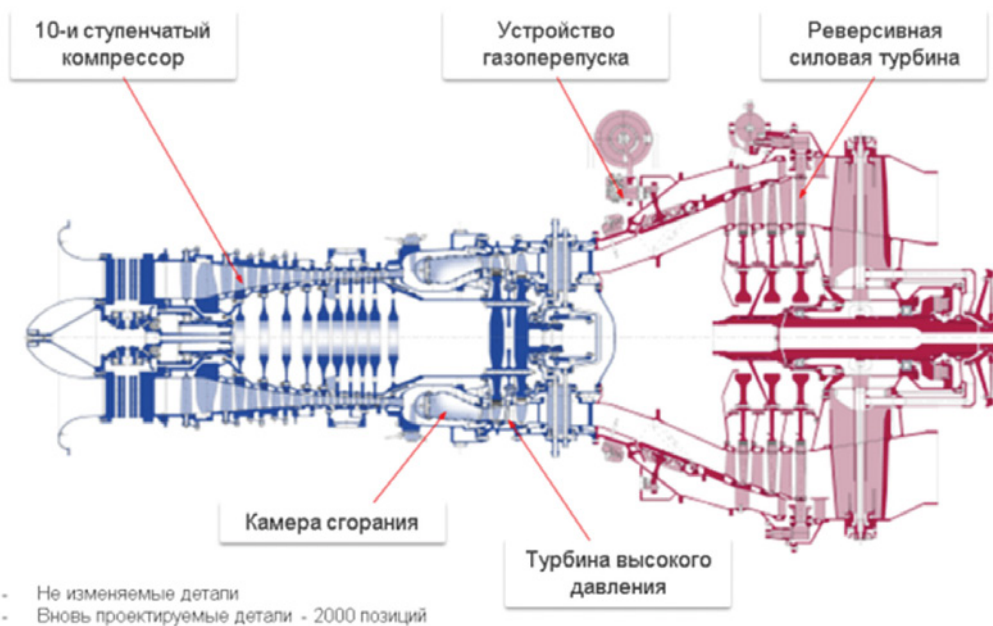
Морской (реверсивный) газотурбинный двигатель М70ФРУ-Р
